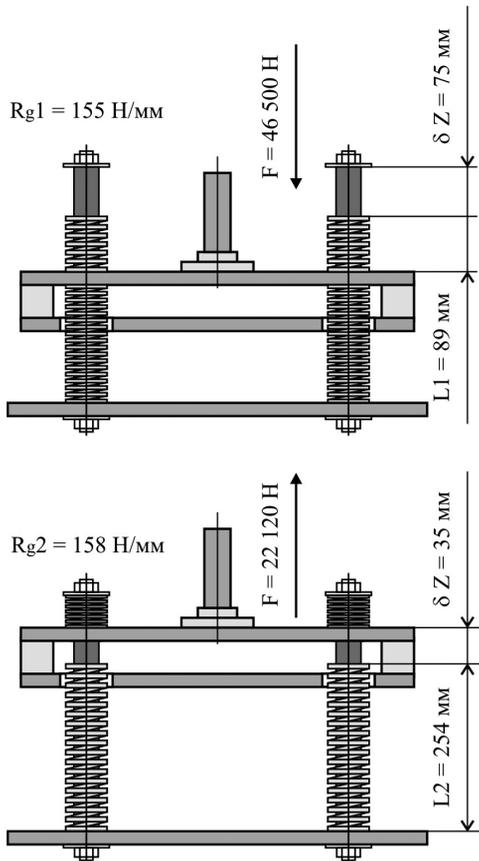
Принцип работы механизма подачи усилия на сварочный инструмент
